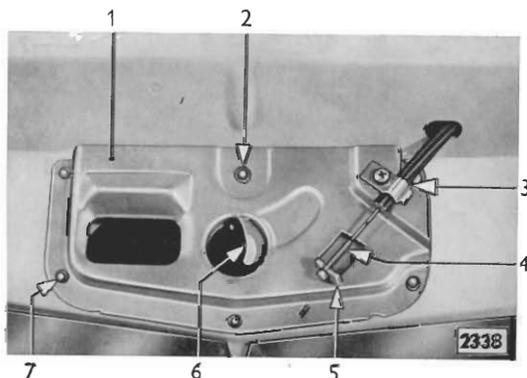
Befestigung des Bowdenzuges für Haubenentriegelung am Haubenschluß
